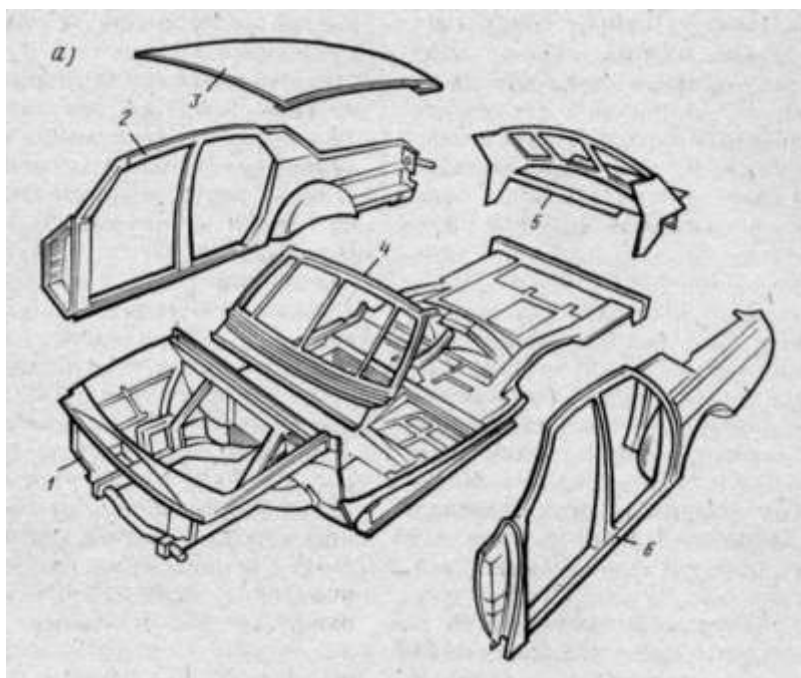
Сборка корпуса кузова легкового автомобиля ГАЗ: *a* — основные узлы корпуса кузова
